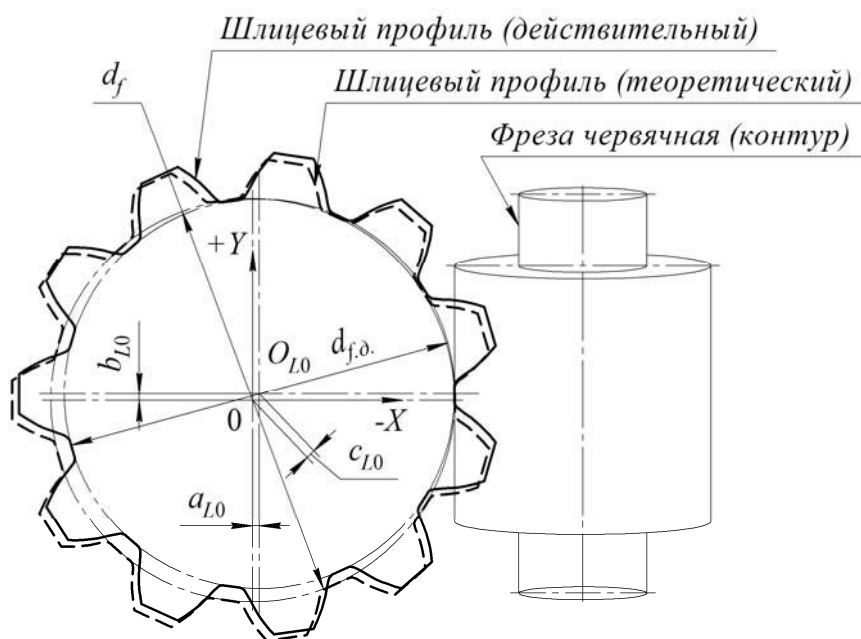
Схема взаимного расположения заготовки относительно фрезы
